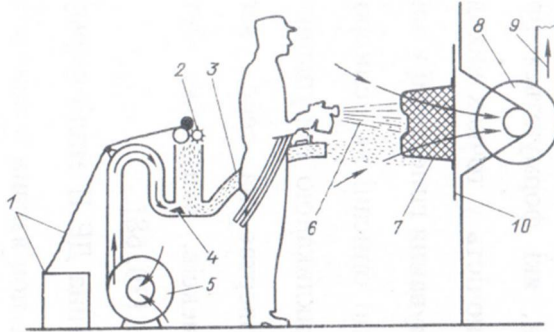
Машина для виготовлення заготовок з припливною камерою
